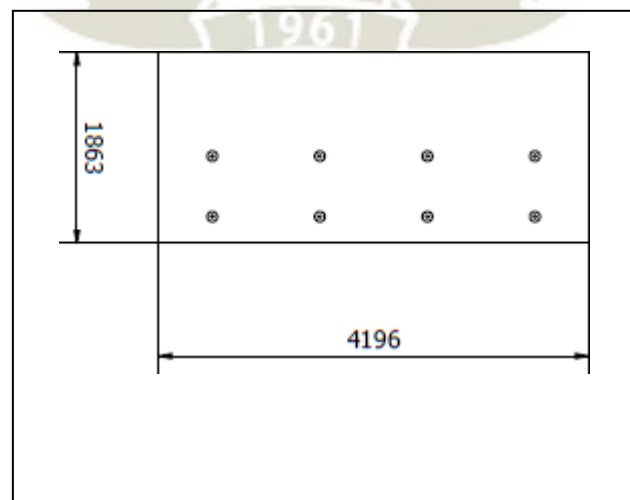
Plancha principal extensión metálica. Fuente: Elaboración propia.
